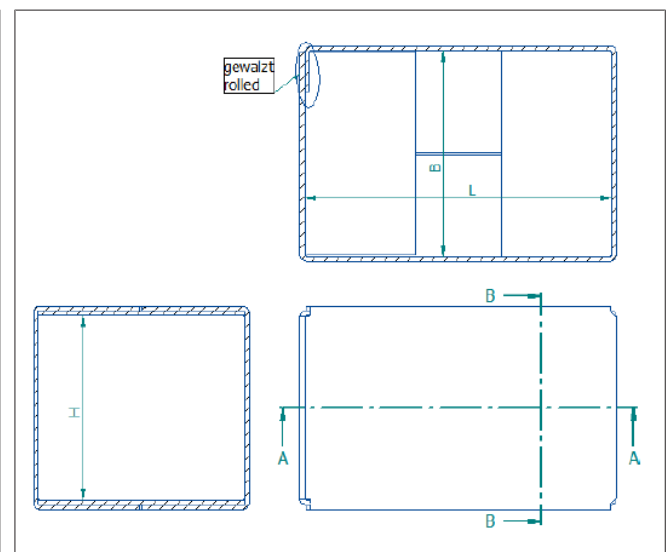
Caixa de cartão com tampas dobráveis - Dimensões
